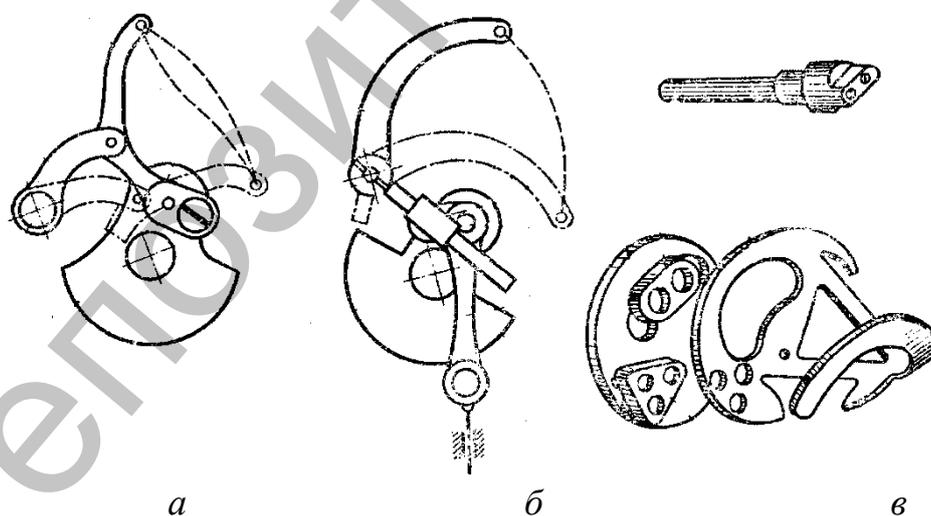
Нитепритягиватели машин челночного стежка: а – шарнирно-стержневой; б – кулисный; в – вращающийся
